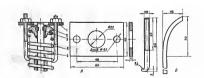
Приспособление для снятия пружин клапанов: а) 1- пластина; 2- тарелка; 3- сухари; 4- крюх; 5- пружина; 6 поддержка.
